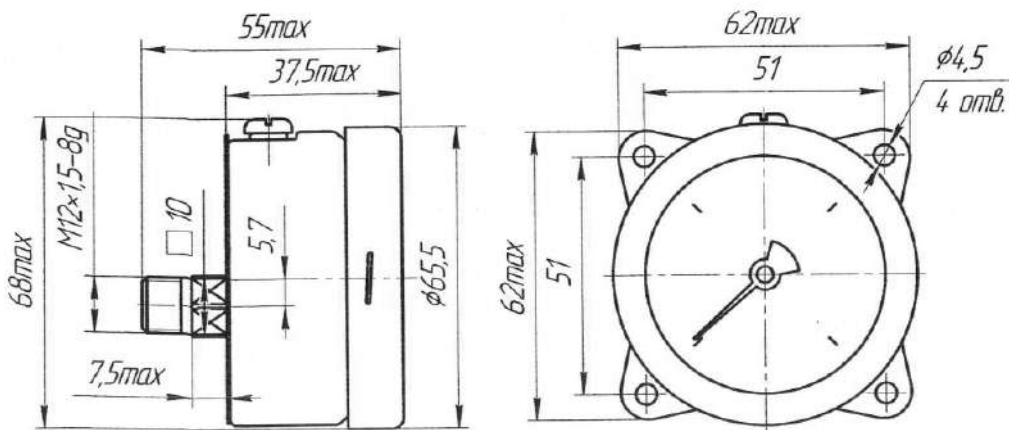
Габаритные и присоединительные размеры приборов с осевым расположением штуцера с фланцем
